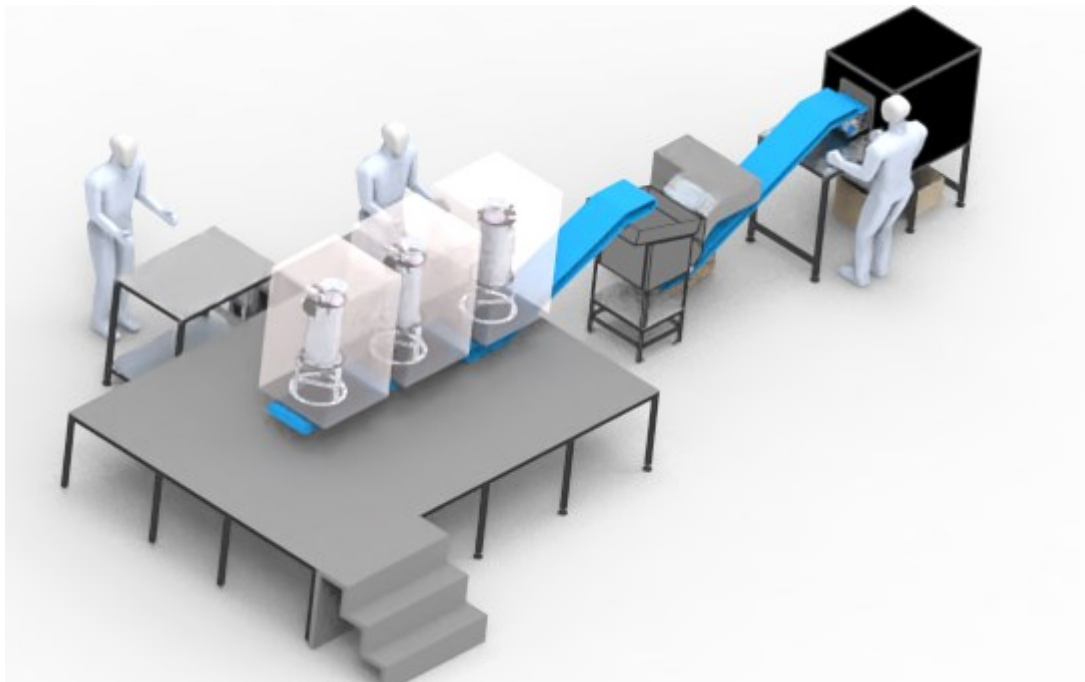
Layout prototipale del primo sottoblocco del blocco 2 (vista assometrica 2)
